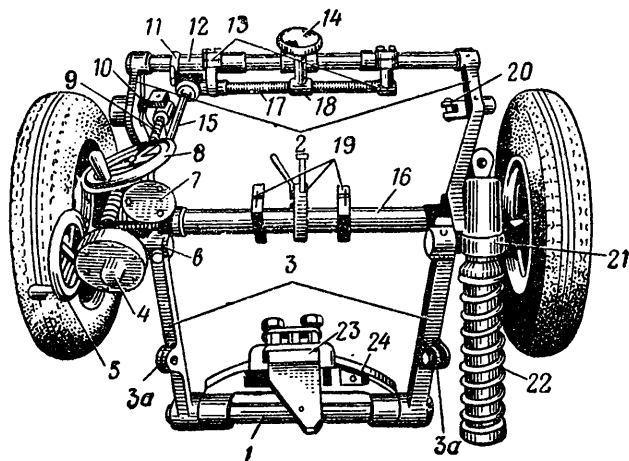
Лафет старой конструкции (С607) (вид сверху):
